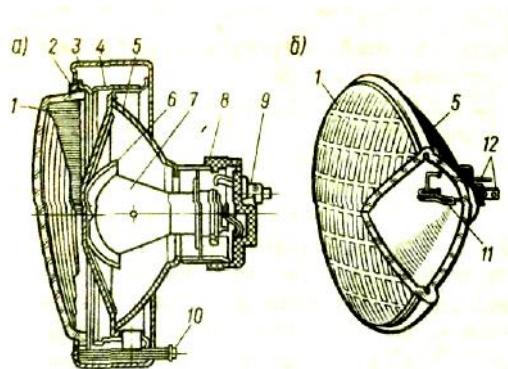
Специальные фары: а — противотуманная фара, б - лампа-фара; 1 — рассеиватель, 2—резиновая прокладка; 3 — ободок. 4 — установочное кольцо, 5—рефлектор, 6 — экран с держателем; 7 — лампа, 8 — патрон. 9 — вывод пружинящего контакта; 10 — винт для регулировки фары. 11 — вольфрамовые спирали. 12—выводы спиралей
